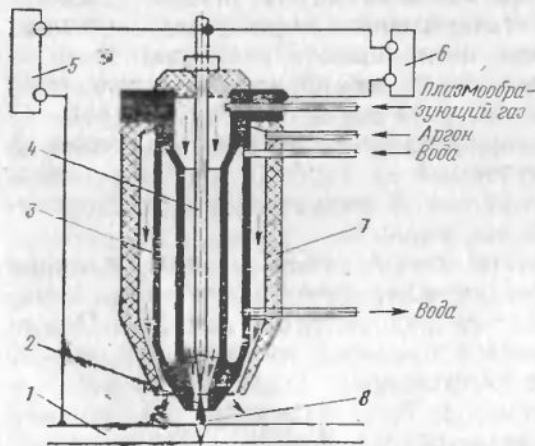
Схема работы плазмотрона при микроплазменной сварке
